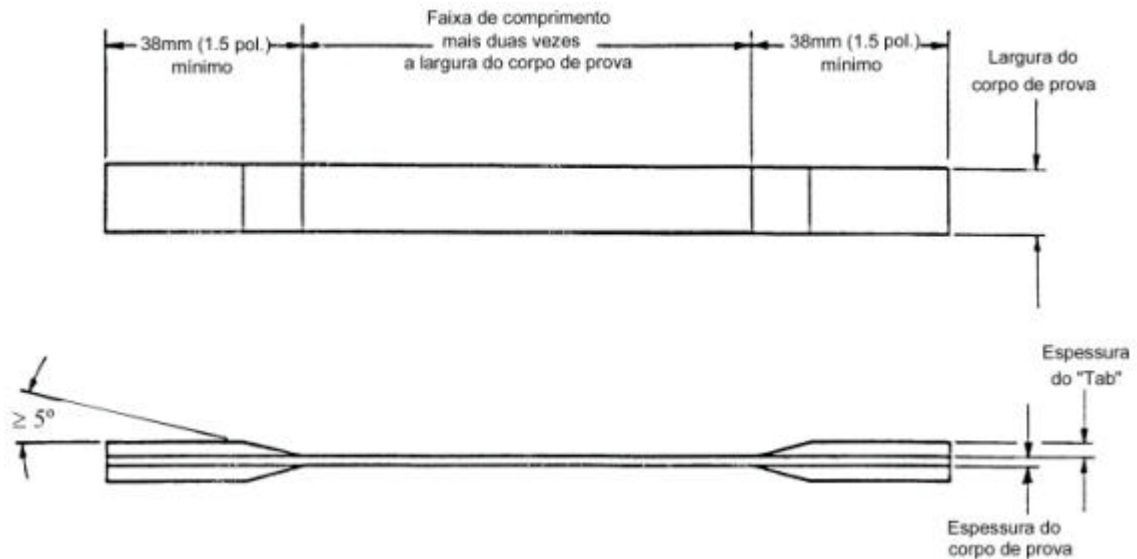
Geometria do corpo de prova utilizado no ensaio de tração.
